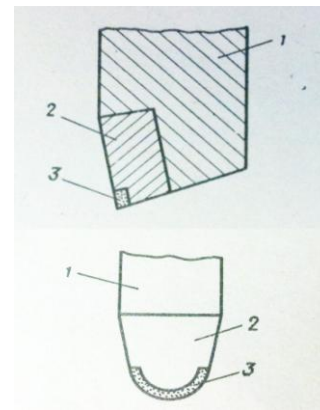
Схема резца для горных пород с алмазной режущей кромкой [6]
